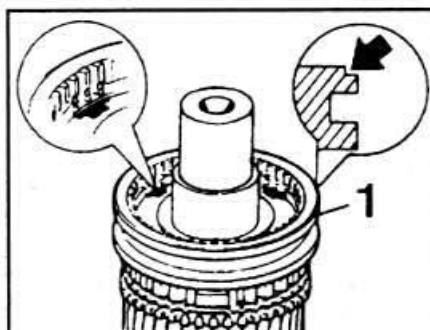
Установка скользящей муфты синхронизатора III и IV передач:
